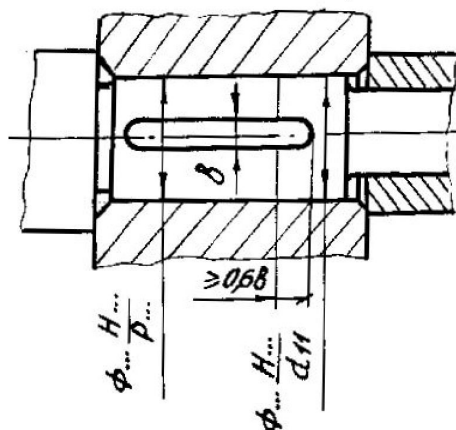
Посадочное место вала под неподвижное шпоночное соединение со ступицами зубчатых и червячных колес
